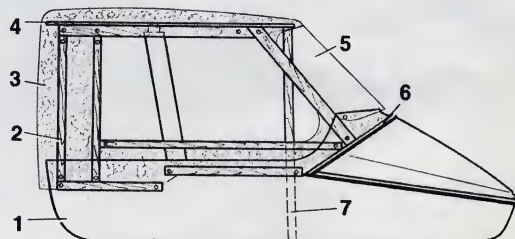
Форма для изготовления колпака: 1 — основание; 2 — рейки 10 × 30; 3 — пенопласт; 4 — лист фанеры; 5 — заготовка ветрового стекла; 6 — резиновый упор-ограничитель; 7 — стойка.
